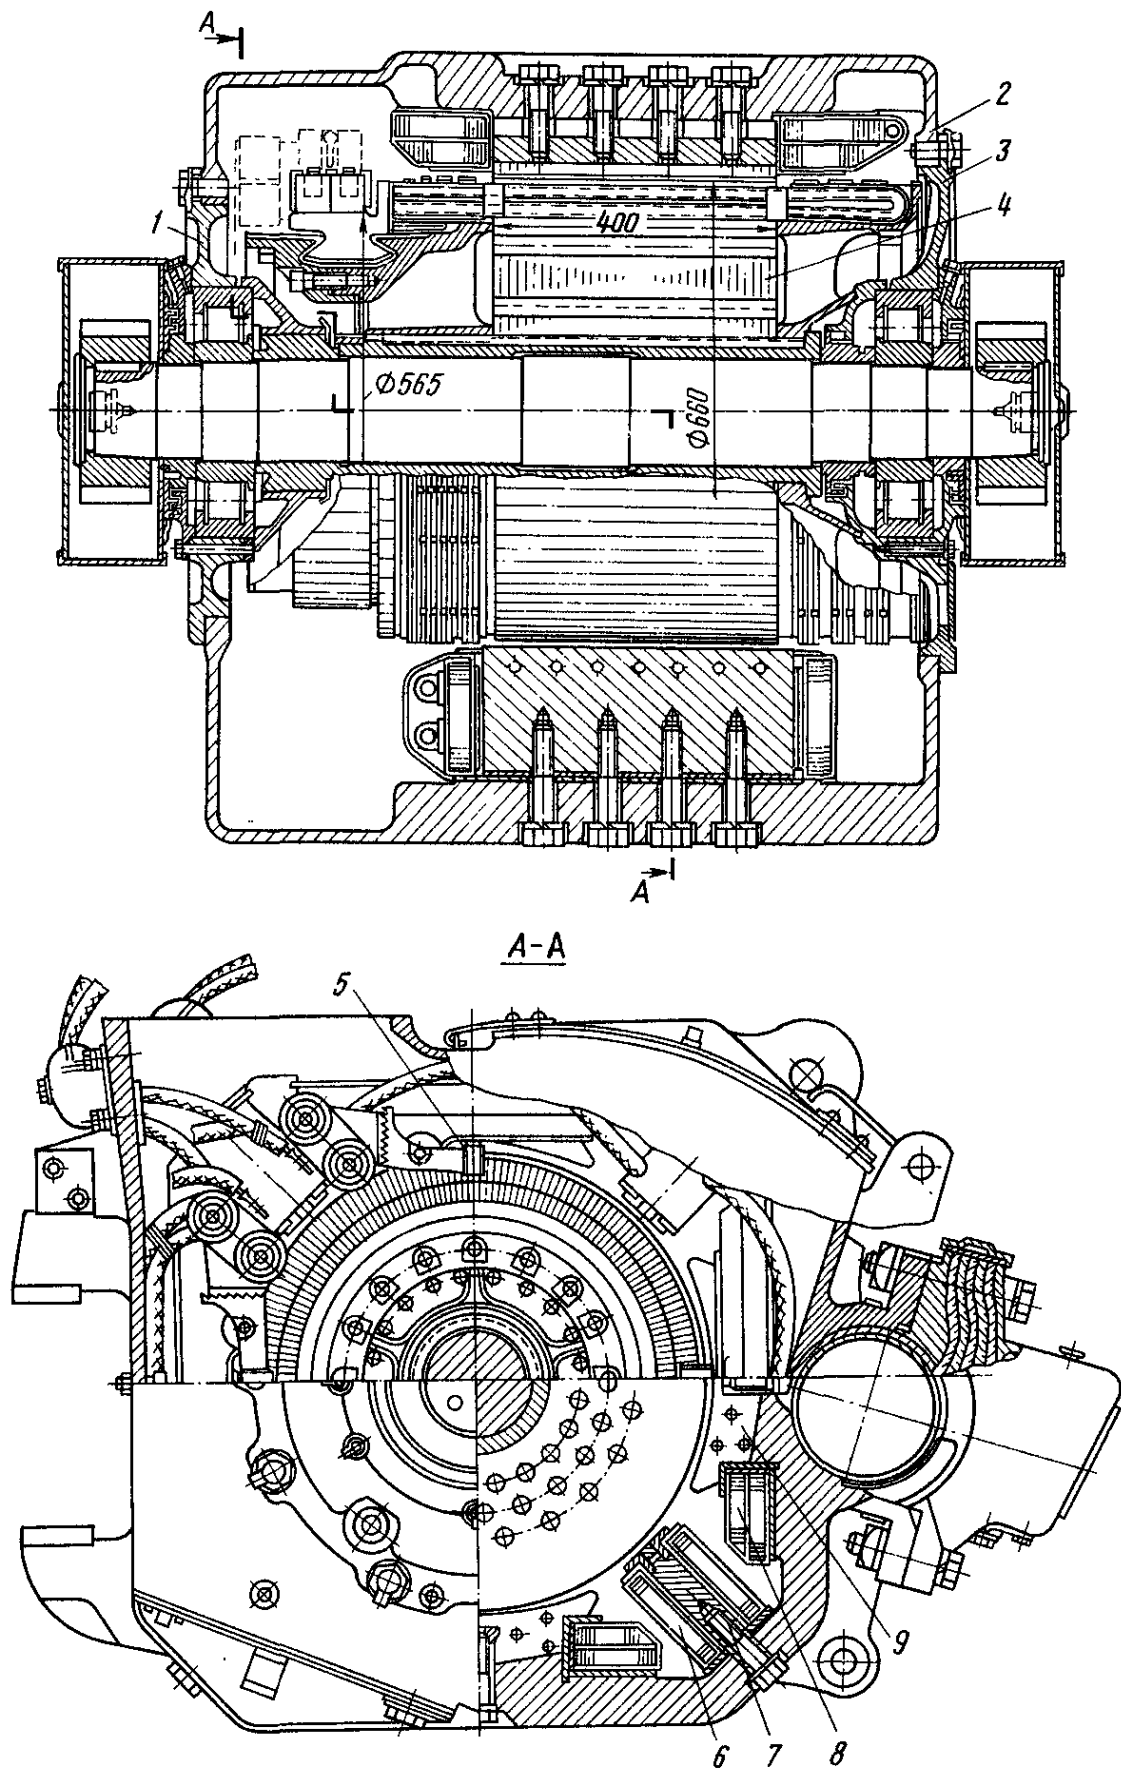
Продольный и поперечный разрезы двигателя НБ-406Б:
